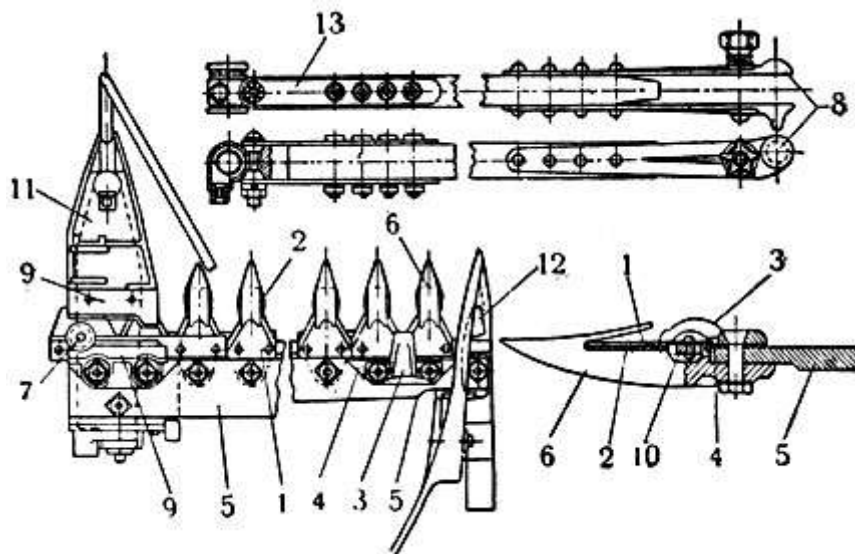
Режущий аппарат жатки: 1 - сегмент ножа; 2 - вкладыш пальца; 3 - нажимная лапка; 4 - пластинка трения; 5 - пальцевый брус; 6 - палец; 7 - головка ножа; 8 - ложечка шатуна; 9 - направляющие крышки; 10 - спинка ножа; 11 - внутренний башмак; 12 - наружный башмак; 13 - шатун
